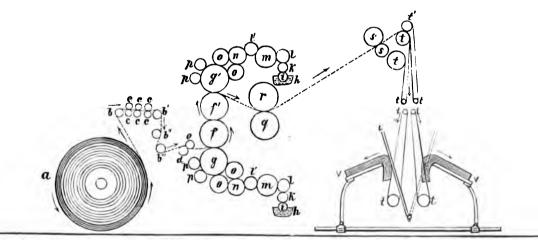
Durchichnittszeichnung ber Rotationsichnellpreffe mit Auslegeapparat aus ber Raichinenfabrit Augeburg.
